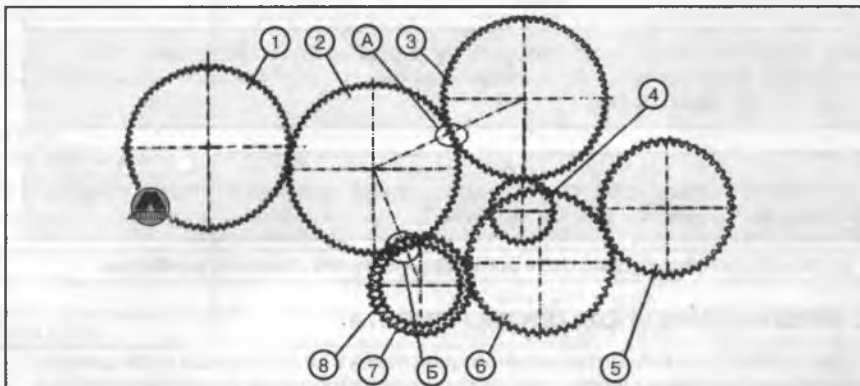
Расположение распределительных шестерен: 1. Шестерня ТНВД; 2. Промежуточная шестерня 1; 3. Шестерня распредвала; 4. Шестерня масляного насоса; 5. Шестерня компрессора; 6. Промежуточная шестерня 2; 7. Шестерня коленвала 1; 8. Шестерня коленвала 2; А. Установка меток шестерни распредвала и промежуточной шестерни 1; Б. Установка меток промежуточной шестерни 1 и шестерни коленвала 2.
